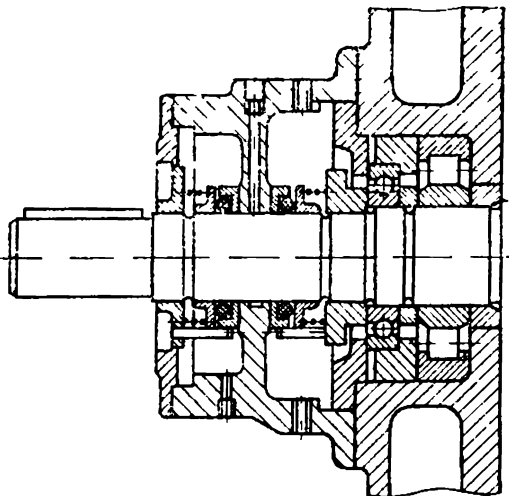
Уплотнение вала газового пластинчатого компрессора с водяным охлаждением
